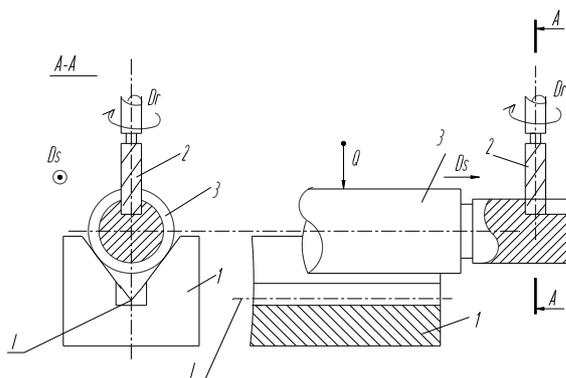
Пример технологической базы вала. 1 - призма (элемент приспособления к фрезерному станку); 2 - шпоночная фреза; 3 - заготовка вала со шпоночным пазом
